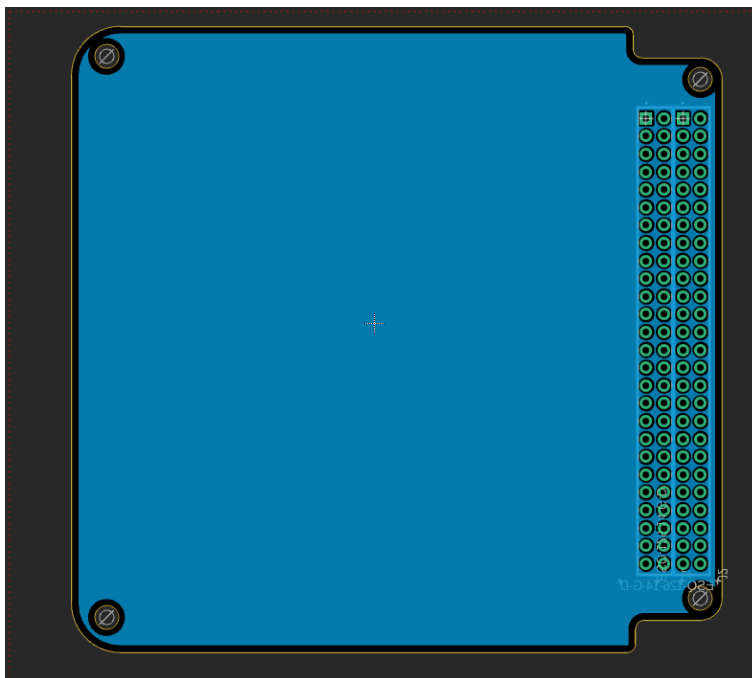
PCB básico y en blanco diseñado para el prototipo.
